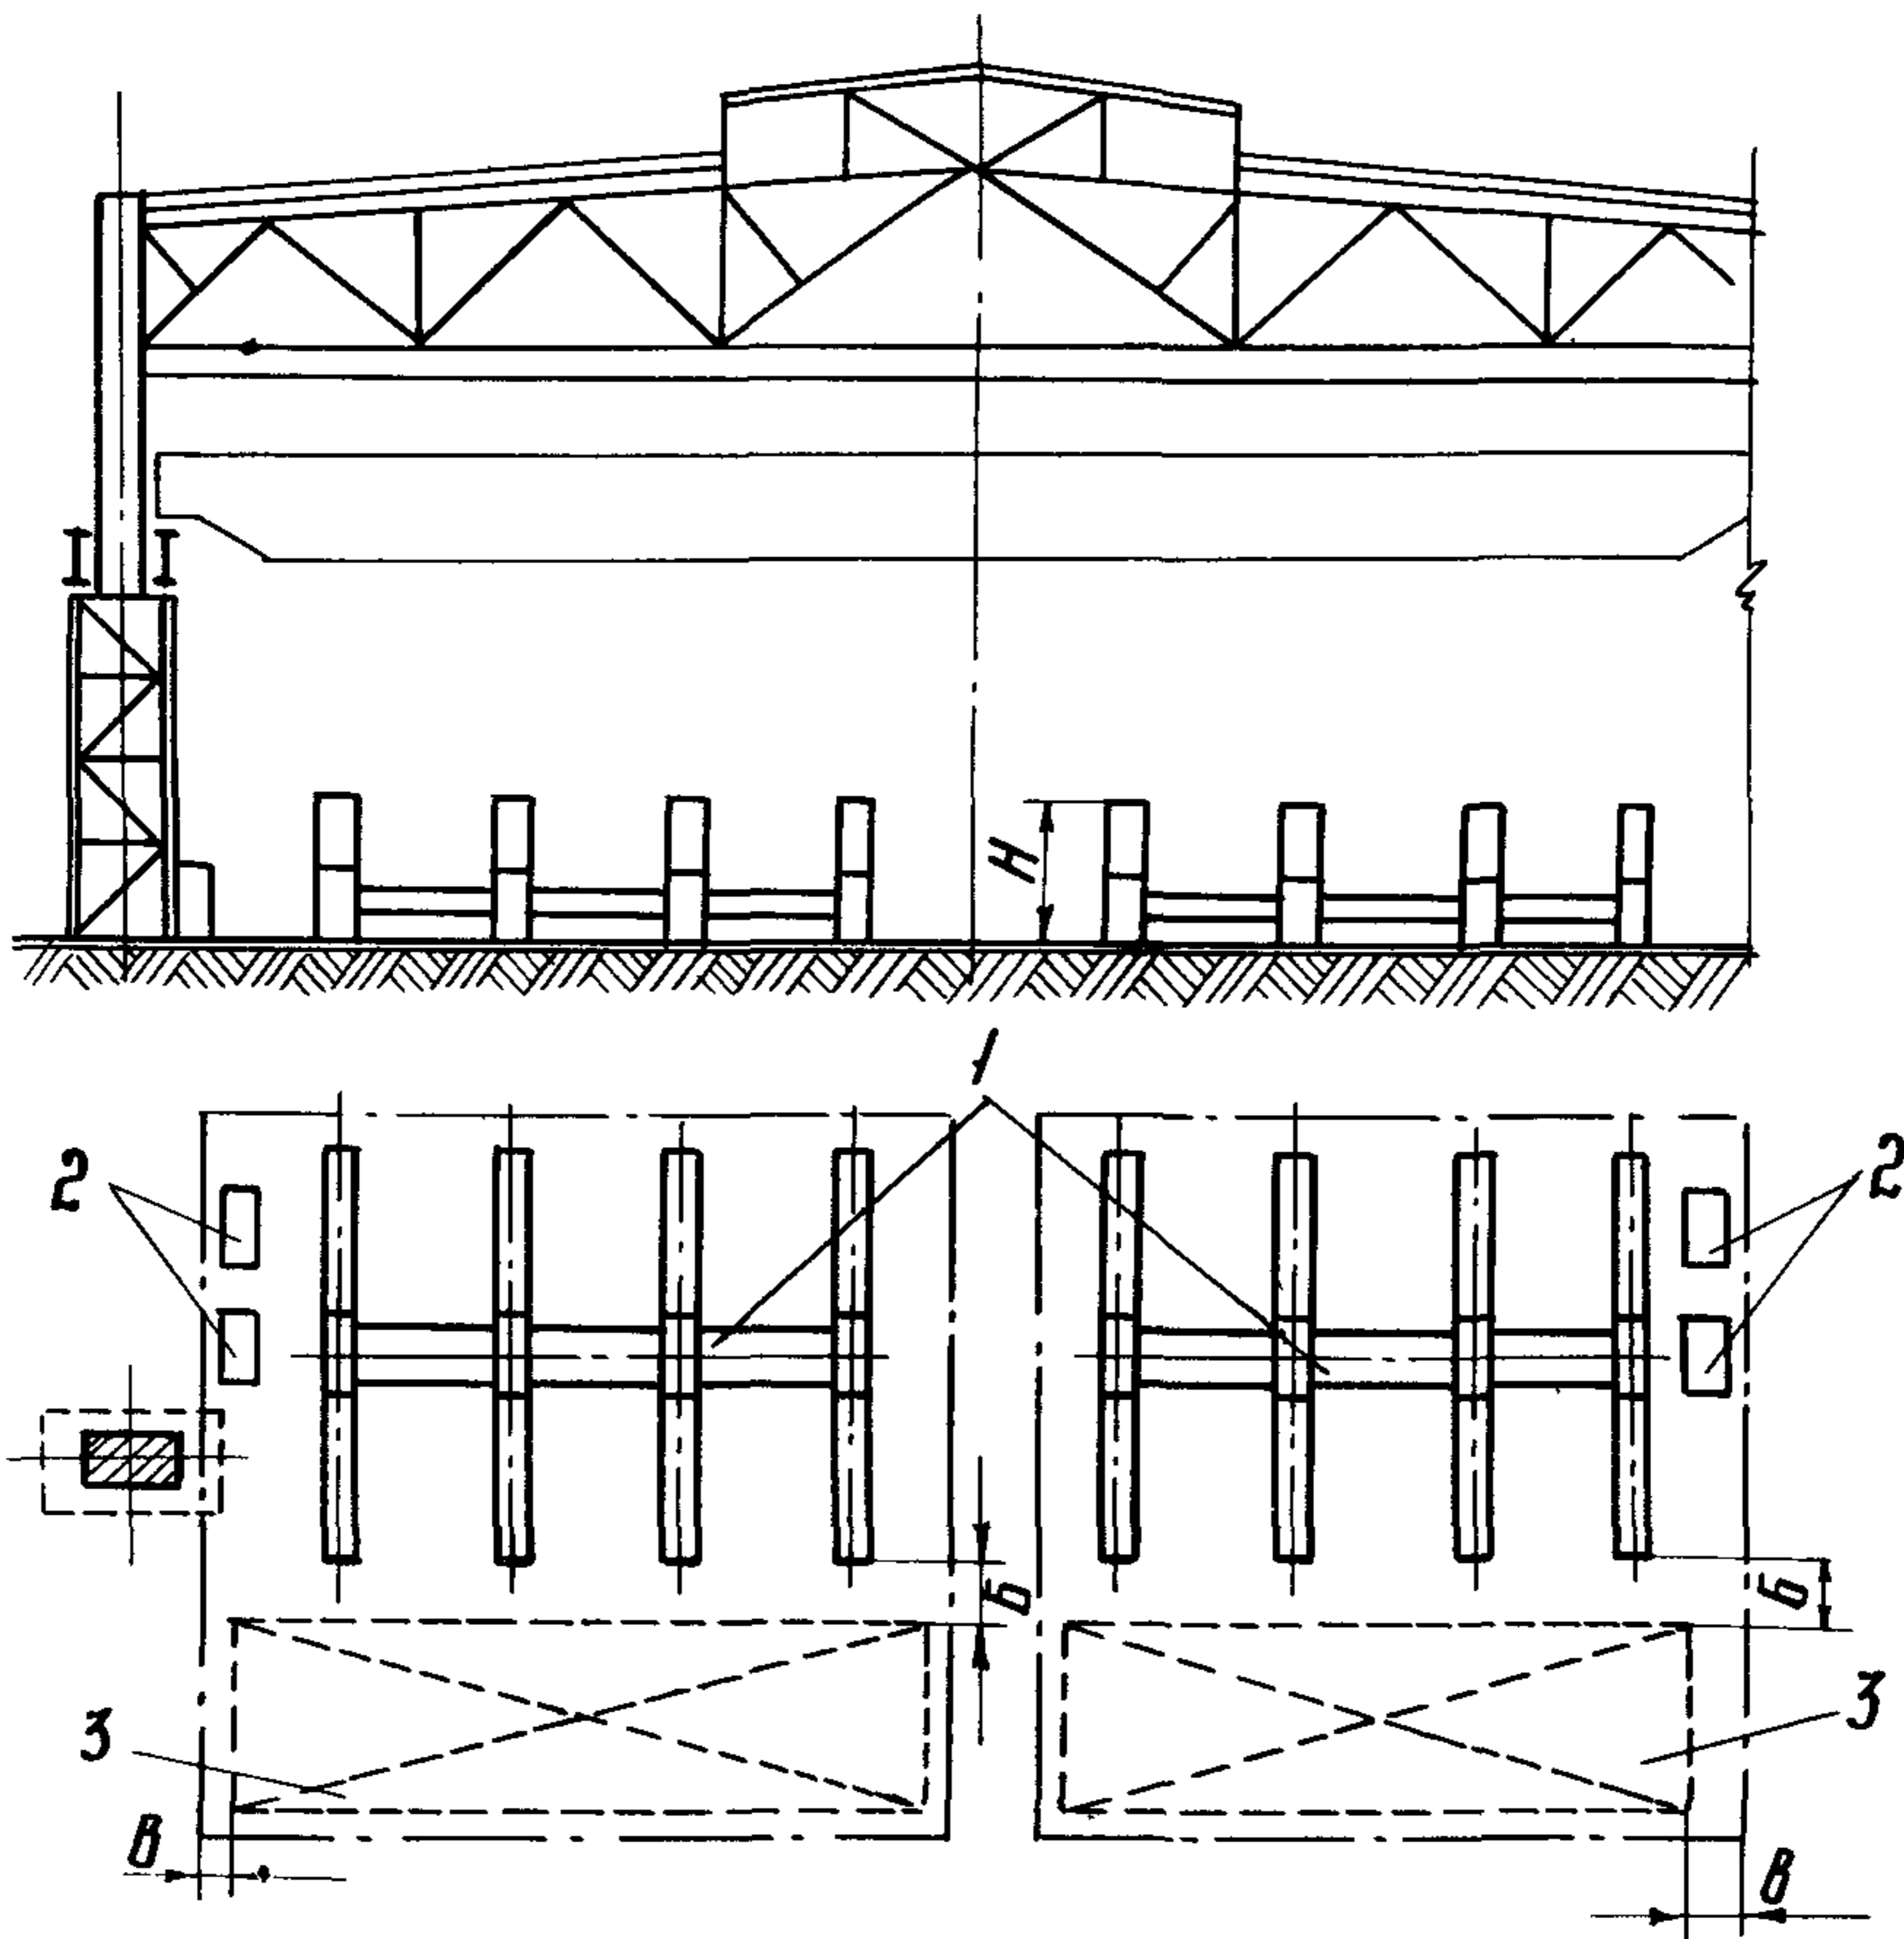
Размещение участка для сварки конструкций в поперечном пролете:
